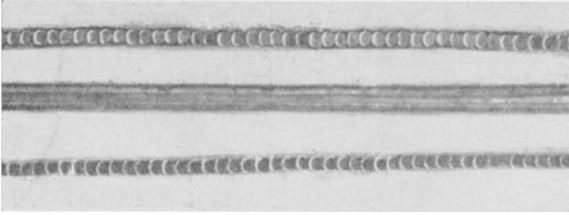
Aussehen von mit Rollenelektroden geschweißten Nähten.
